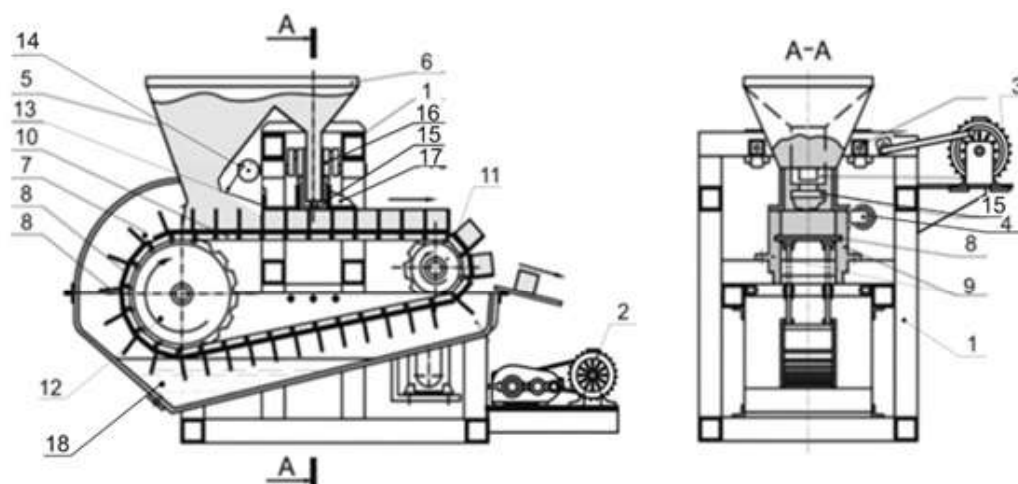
Общая схема установки: 1 – рама; 2–4 – электродвигатели; 5 – бункер; 6 – бункер досыпки порошковой массы; 7 – заполняющая форма; 8 – Г-образные цельные пластины; 9 – две неподвижные щеки с пазами; 10 – конвейер; 11, 12 – ведущая и ведомая звездочки; 13 – предварительно трамбуемая плита; 14 – кривошип; 15 – П-образный нагнетатель (пуансон); 16 – кривошипно-шатунно-коромысловый механизм; 17 – нож из стального уголка; 18 – ванна с водой
